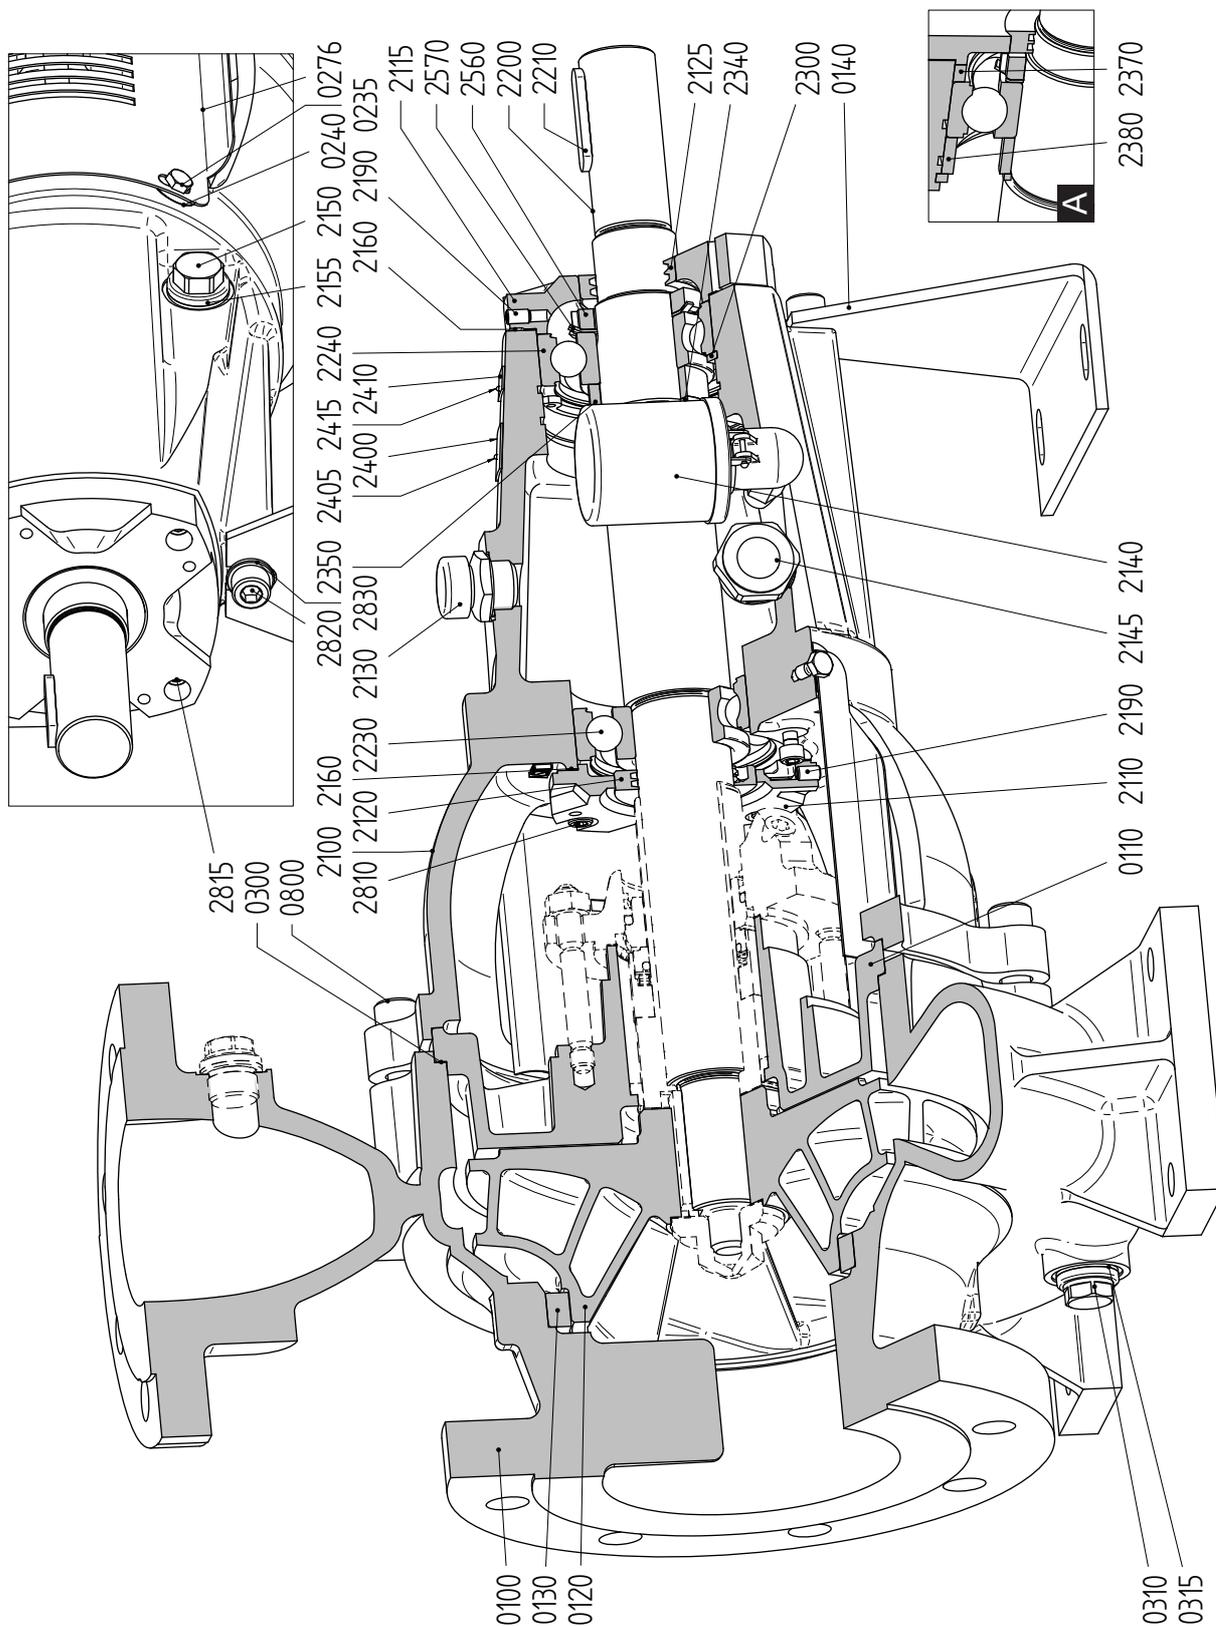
Чертеж в разрезе L3 (A = для группы подшипников 3)
